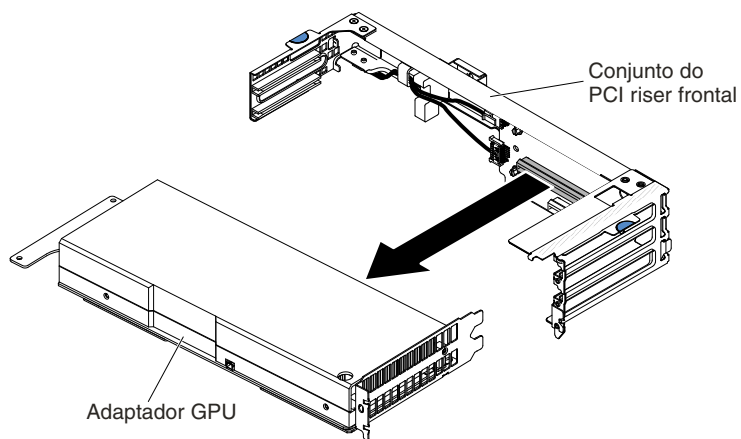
Remoção do adaptador GPU (do conjunto da placa riser PCI frontal)
